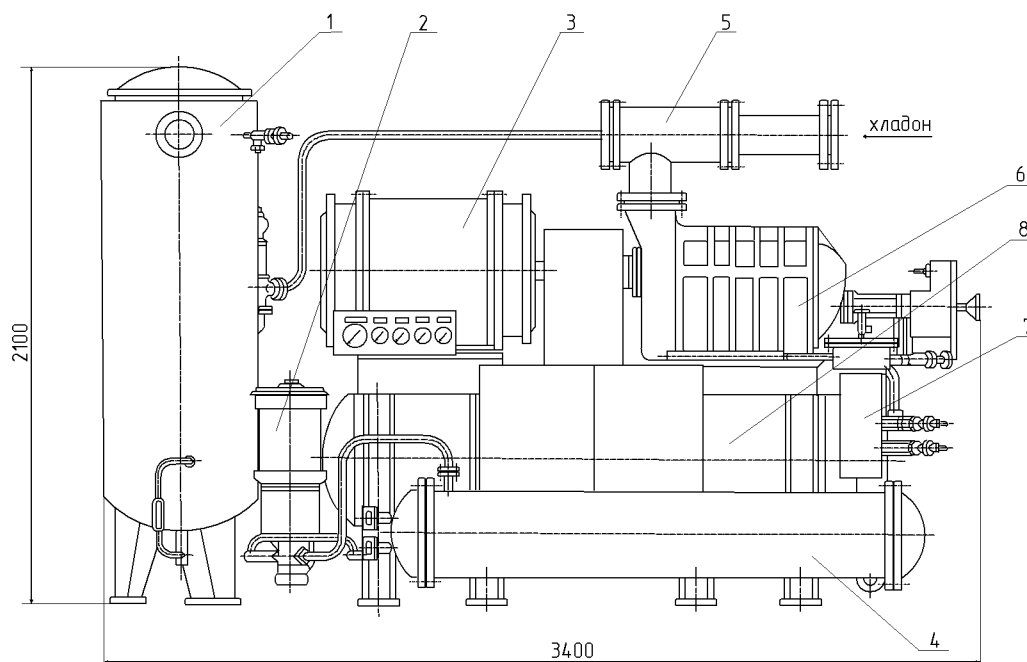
Судновий гвинтовий компресорний агрегат
